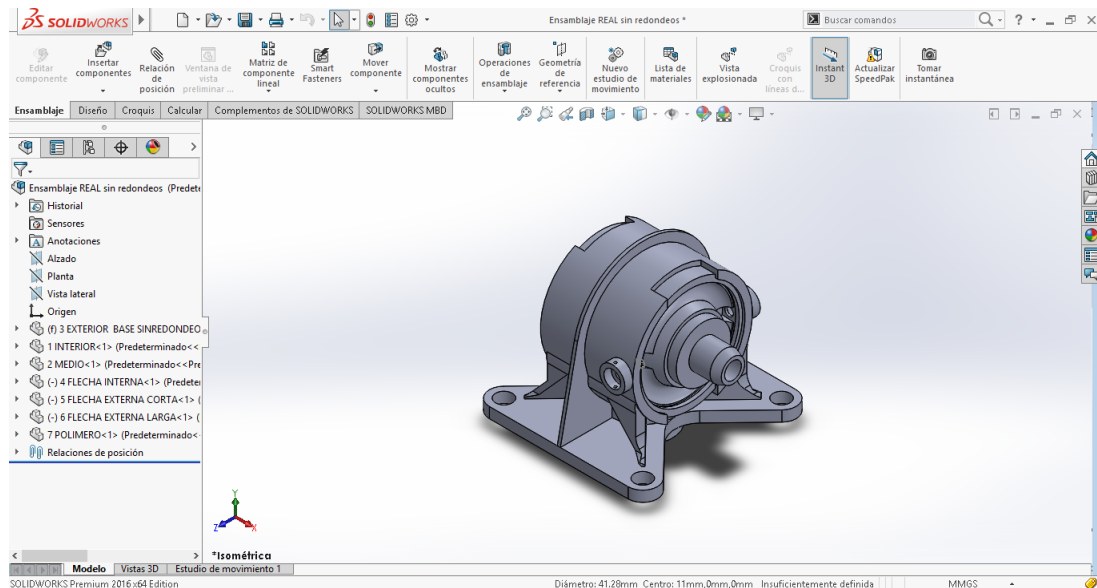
Modificado de pieza 3 y ensamblaje.
